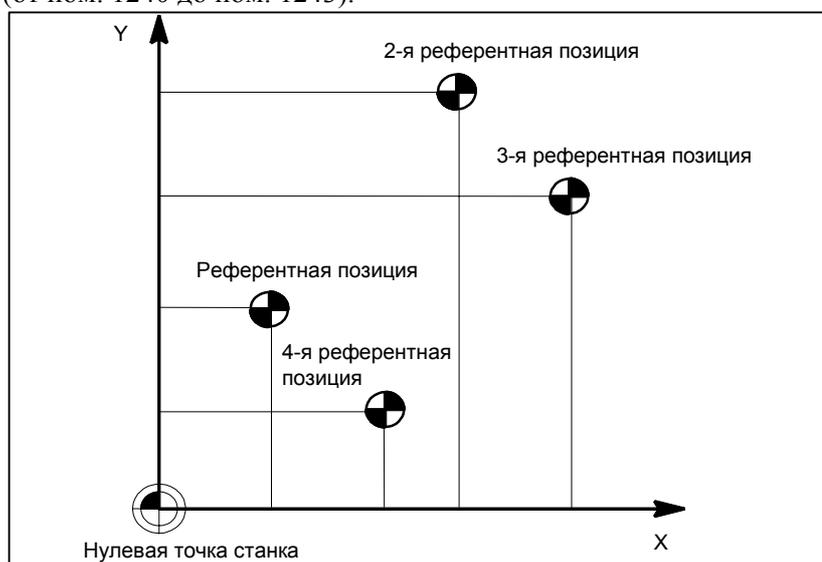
(а) Нулевая точка станка и референтные позиции
